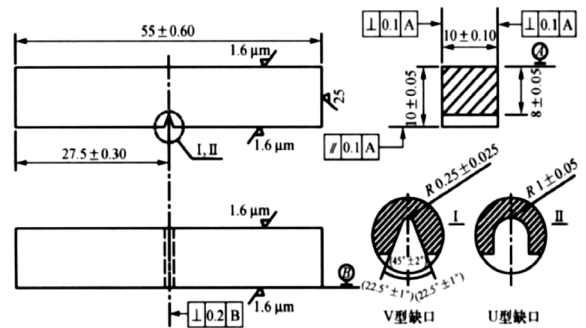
钢轨 U 型、V 型冲击试样缺口尺寸
